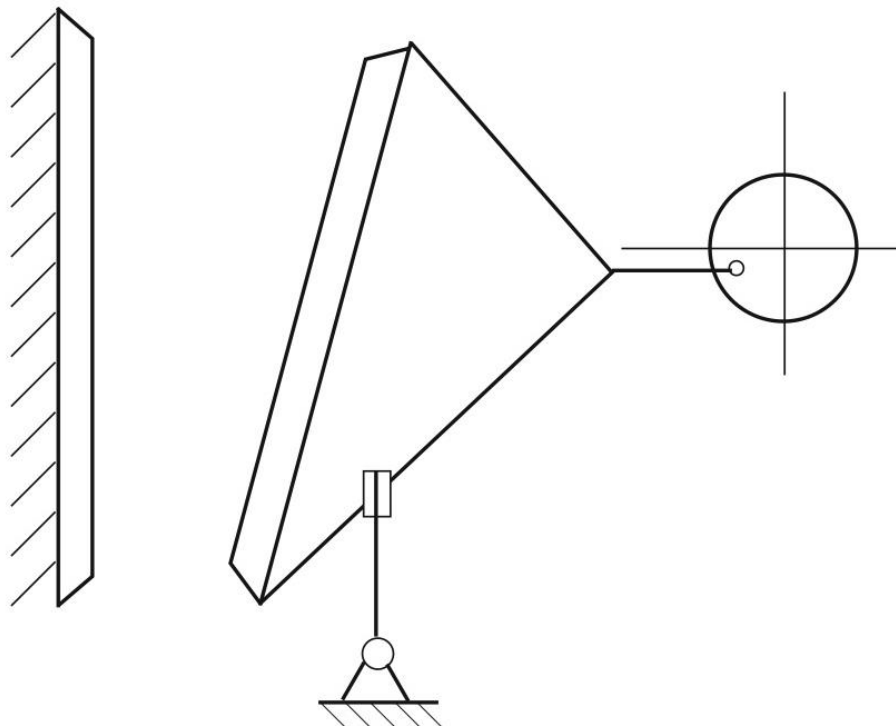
Кінематична схема дробарки фірми «Мюллер» (Німеччина).
